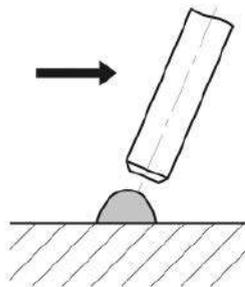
Влияние длины дуги и скорости сварки.
